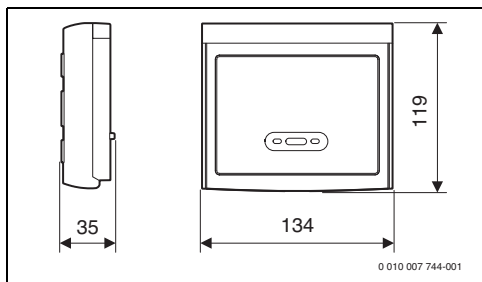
Módulo emisor MBRF, dimensiones en mm
